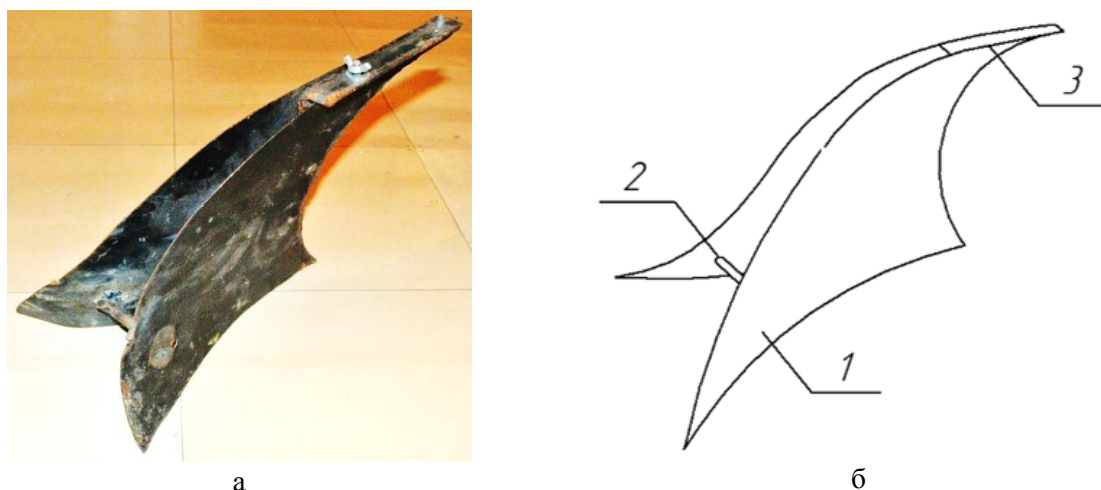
Двусторонний отвал: а – общий вид; б – схема: 1 – крыло двустороннего отвала; 2 – регулировочный винт ширины захвата; 3 – крепление
